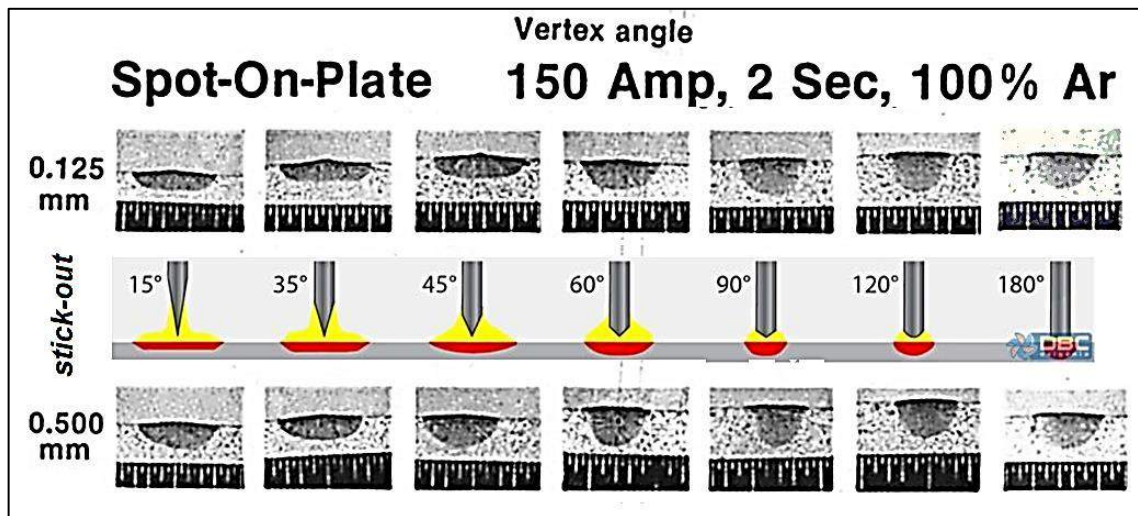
Efeitos do ângulo do eletrodo e da distância “eletrodo-peça” para soldagem *TIG* autógena, adaptado de AWS – Welding Process, 2009.
